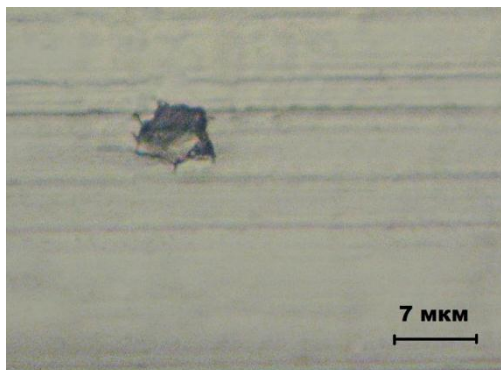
Раковина на поверхности дорожки качения кольца подшипника
